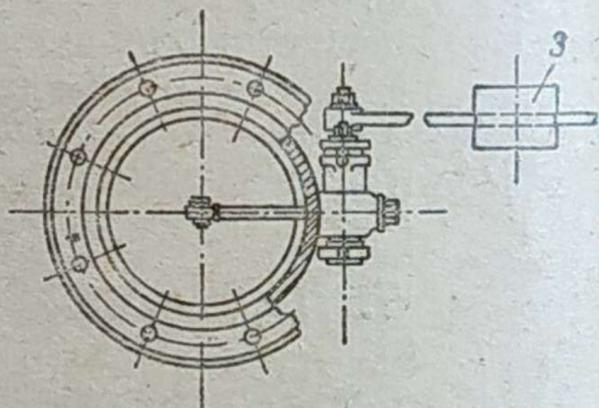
Обратный клапан: 1—корпус клапана, 2—конус клапана, 3—противовес
